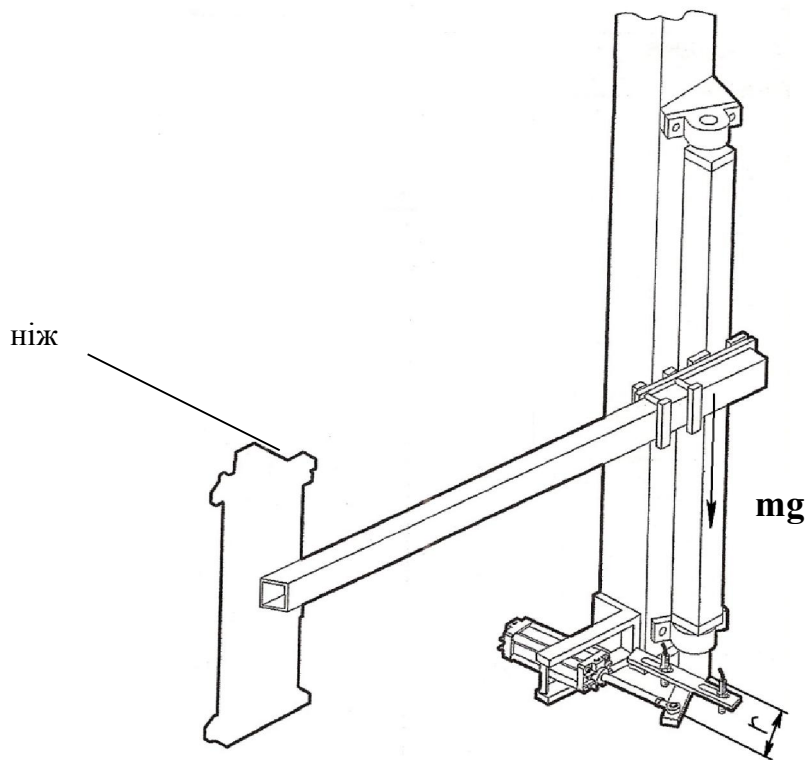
Розрахункова схема для механізму відрізання полімерної розтягувальної плівки
